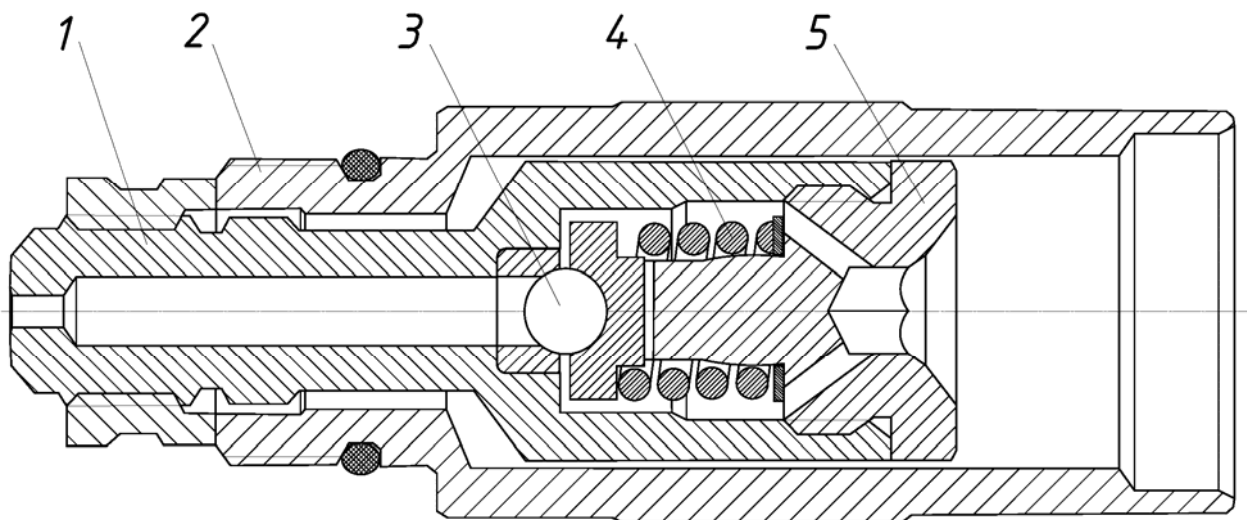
Зворотний клапан системи зливу палива. 1 – корпус клапана; 2 – зовнішній корпус; 3 – кульковий клапан; 4 – притискна пружина; 5 – різьбова пробка
